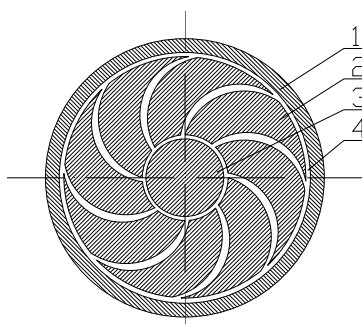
Конструкция твэла с металлическим составным сердечником. 1 – оболочка твэла, 2 – основные лепестки сердечника, 3 – центральный стержень, 4 – жидкий металл.
